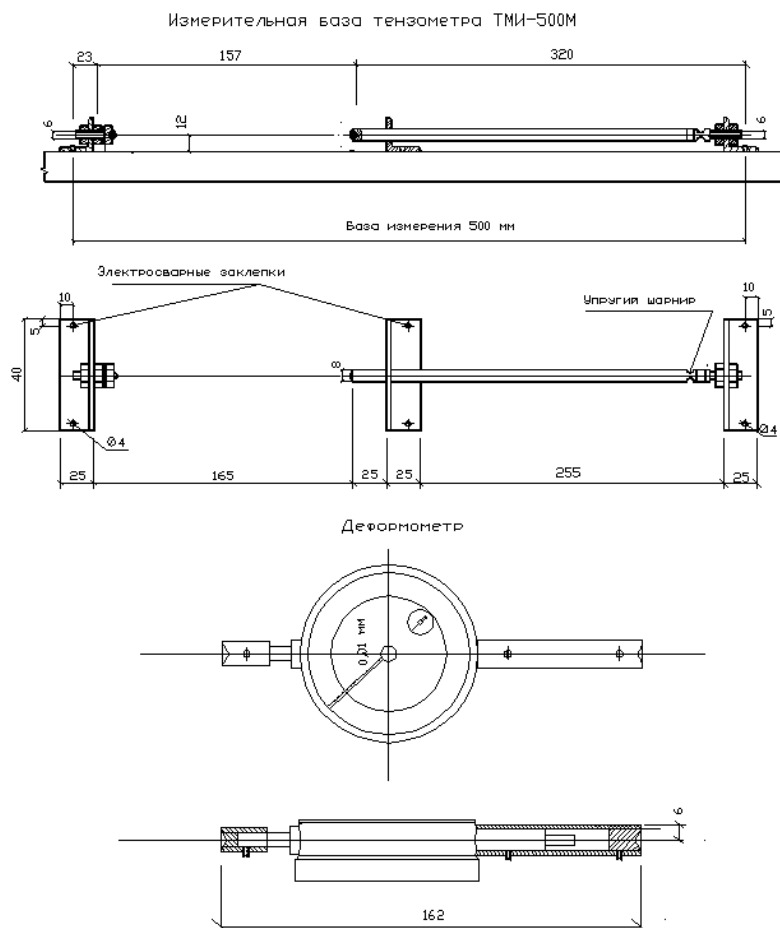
Схема и общий вид механического тензомера ТМИ-500М и деформометра типа ИЧ-10
